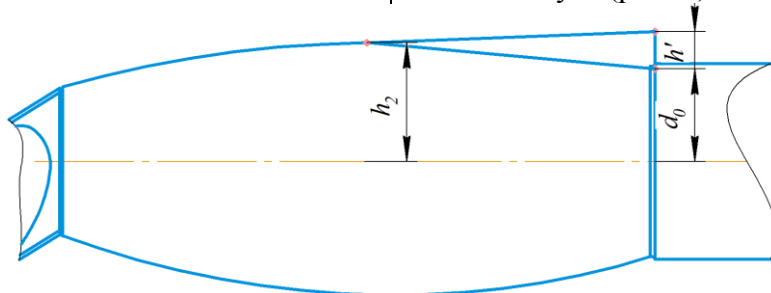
Параметры переходного участка расточного резца с твердосплавной пластиной и дополнительным внешним конусом
